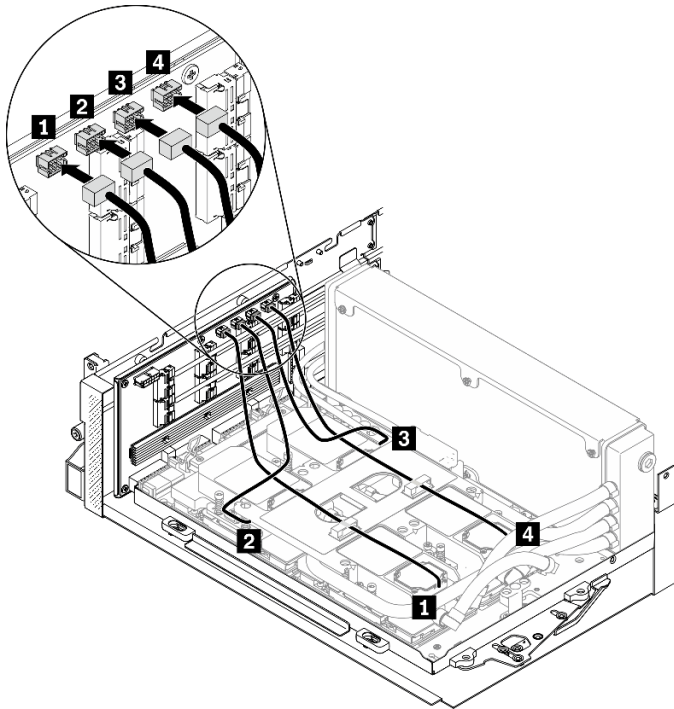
Disposición de los cables de la bomba del conjunto de placa de frío al conjunto de retemporizador: Configuración F
